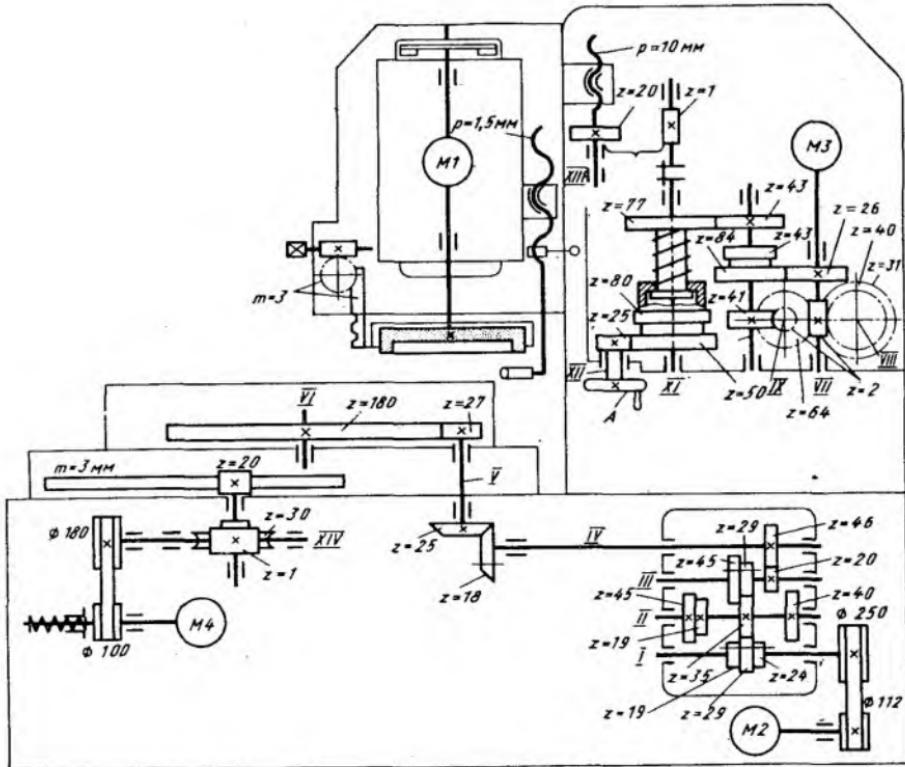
Кинематическая схема плоскошлифовального станка ЗЕ756
